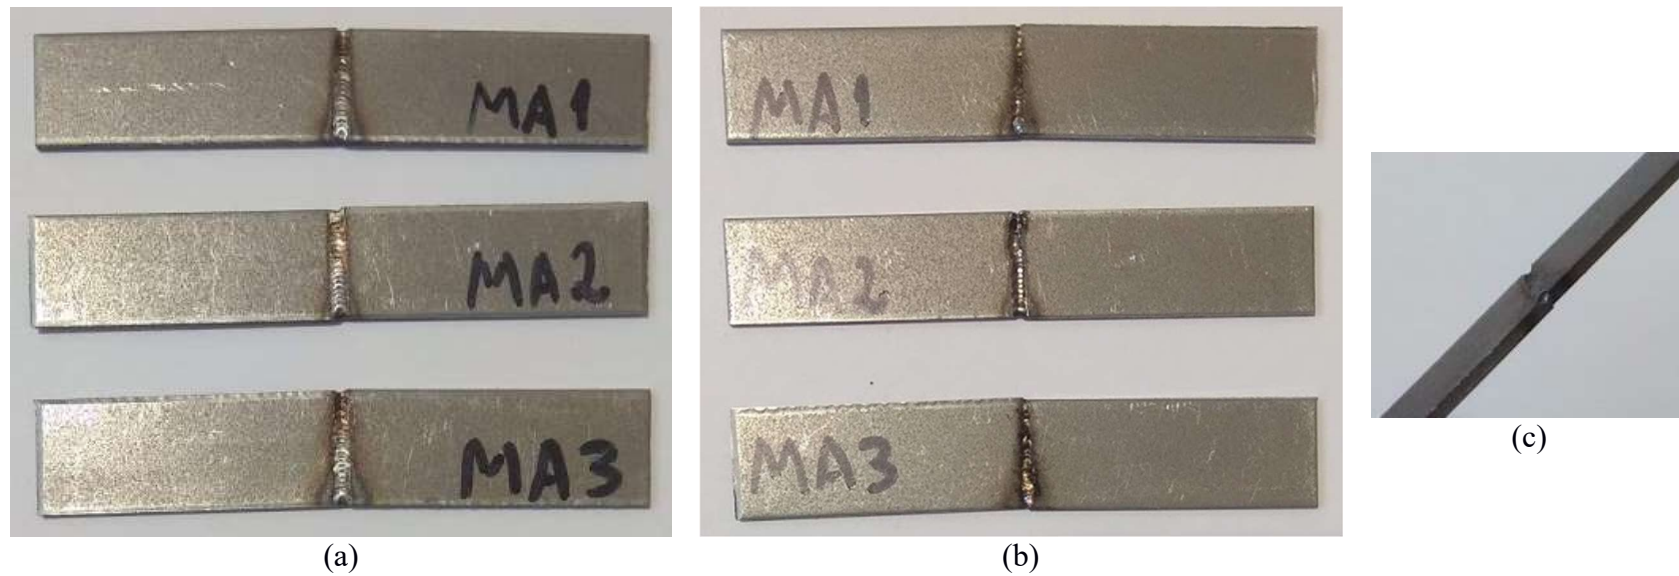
Amostras MA1-MA3. (a) parte superior. (b) raiz da soldadura. (c) abatimento do cordão
